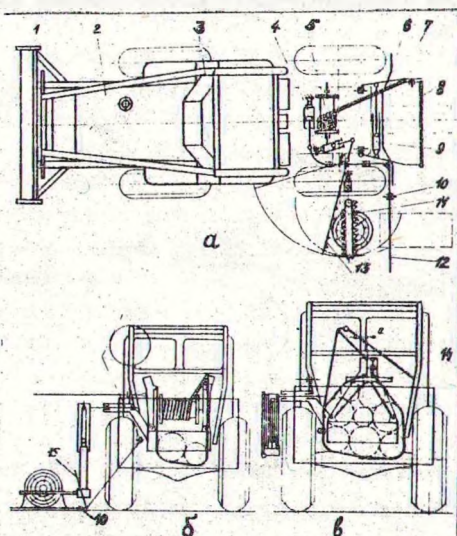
Валочно-трелевочная машина: а-вид сверху; б-вид сзади (после повала дерева); в-вид сзади (в транспортном положении): 1-толкатель; 2-трактор; 3-ограждение; 4, 9-гидроцилиндры; 5-лебедка; 6-штит; 7-раздвижная арка; 8-канат; 10-неполноповоротный шарнир; 11-срезающий механизм; 12-приемно-погрузочный рычаг; 13-валочный рычаг; 14-упорная балка; 15-упор.
